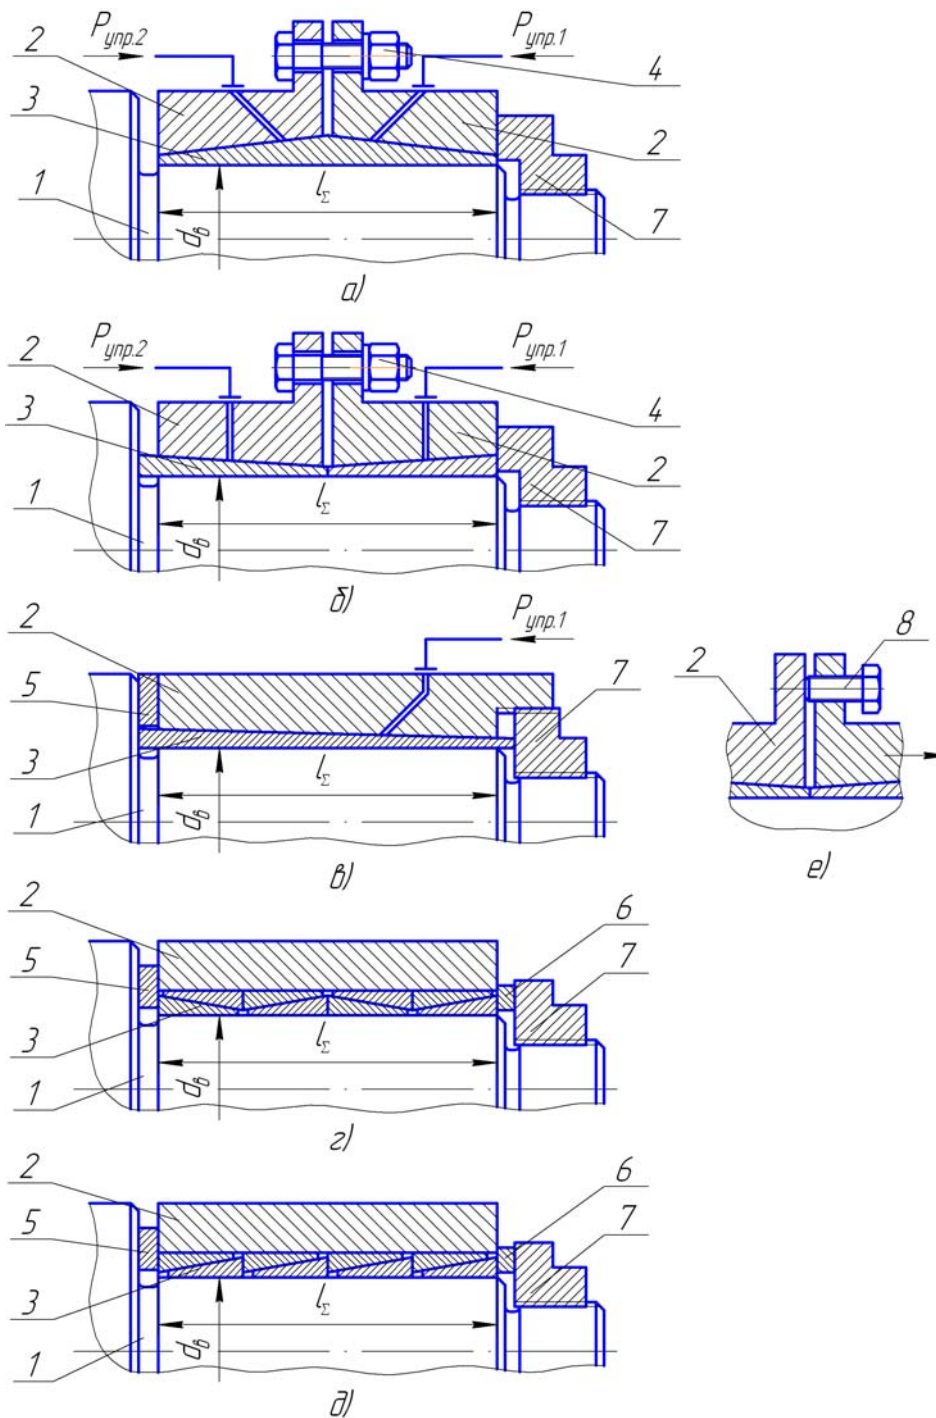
Соединения с натягом разного типа (1 – вал; 2 – втулка основная; 3 – втулка промежуточная; 4 – болты с гайками стяжные; 5 – шайба упорная; 6 – шайба промежуточная; 7 – гайка прижимная; 8 – болт распорный;  $d_{в}$  – диаметр вала;  $l_{с}$  – длина контакта вала с поверхностями втулок):
